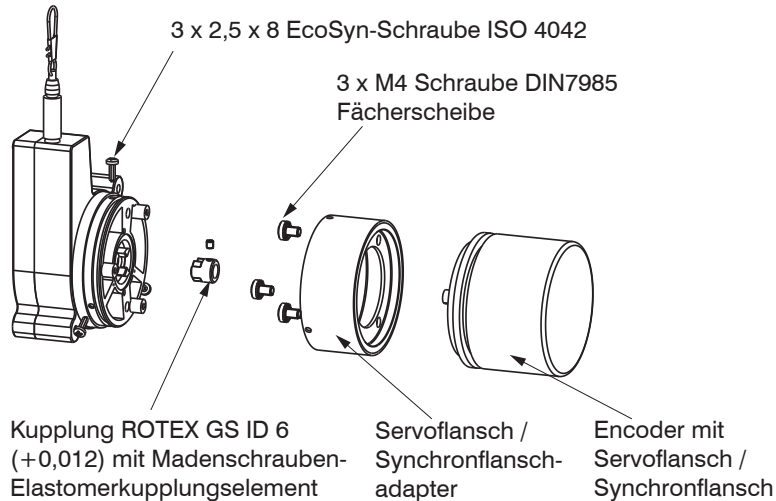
Montage von Adapterflansch und Encoder, WPS-2400-MK60-M
